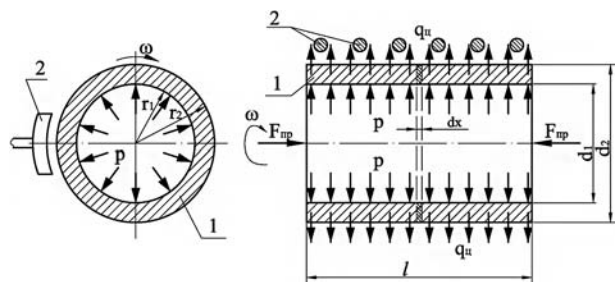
Схема нагружения цилиндрической оболочки:
